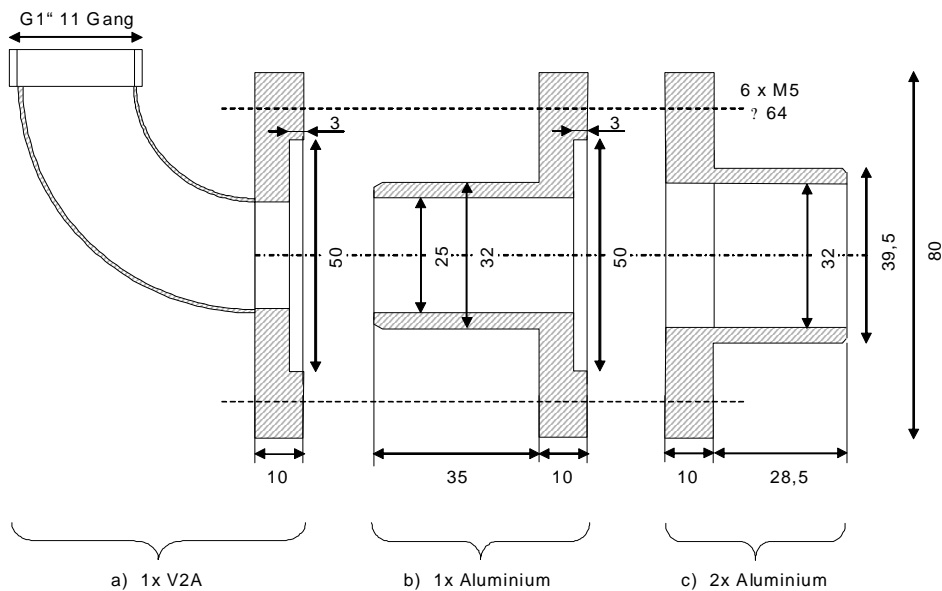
Flansche für Rotameter (a), für Gebläse (b) und am Kanal (c)
